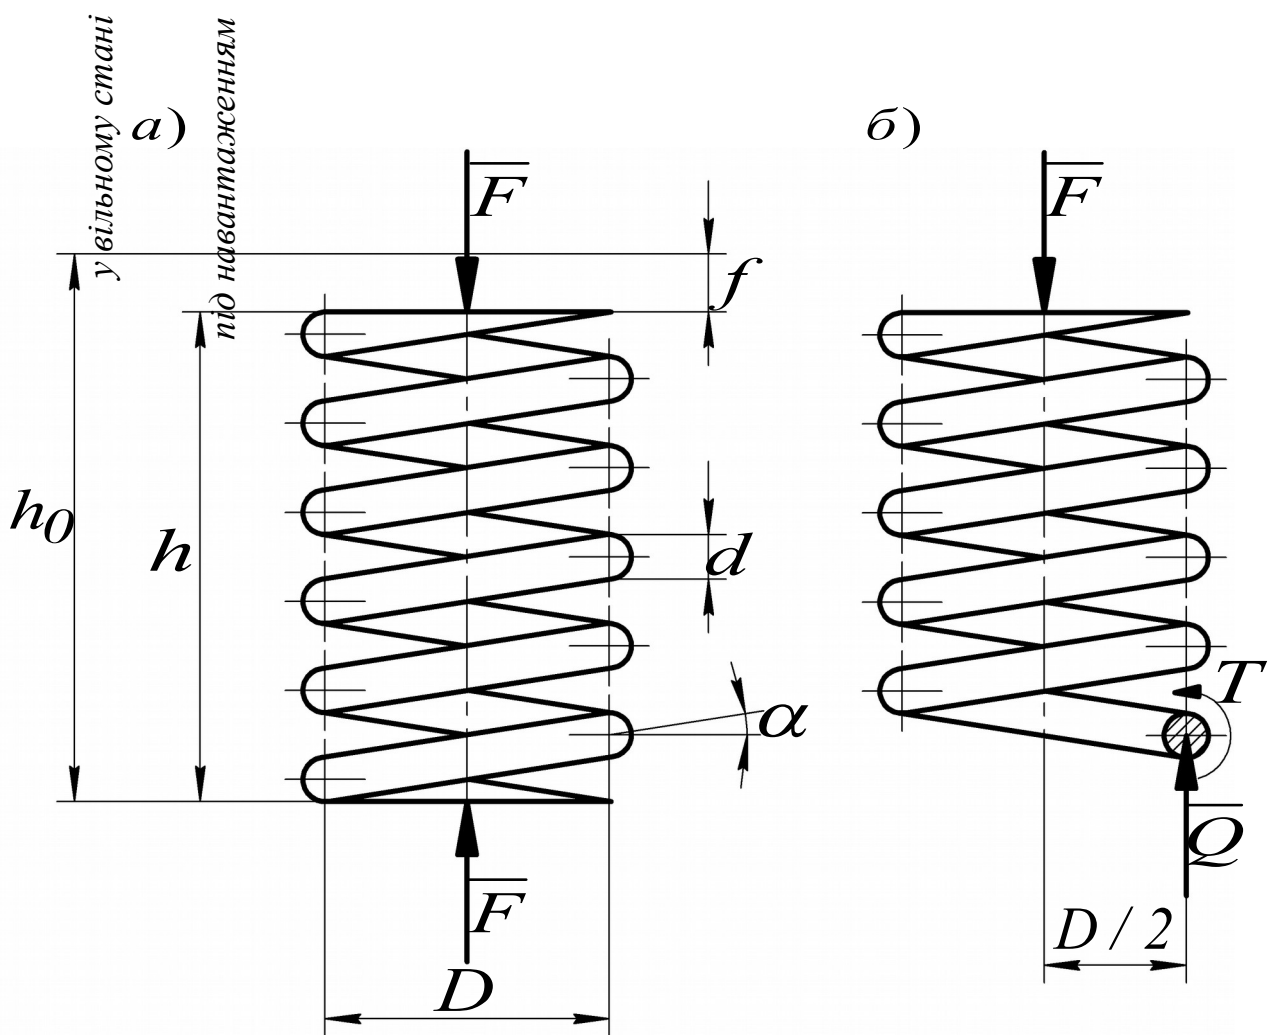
Розрахункова схема циліндричної гвинтової пружини
